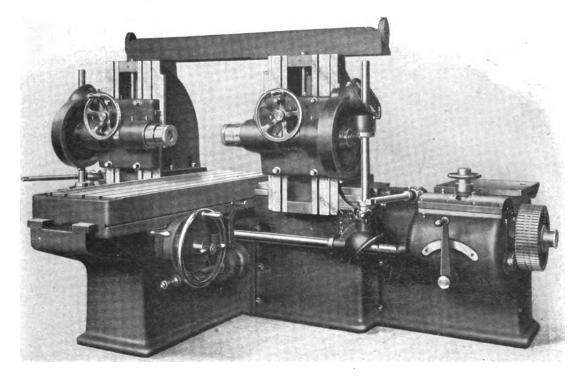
Doppel-Langfräsmaschine von Gildemeister & Co., Bielefeld.
